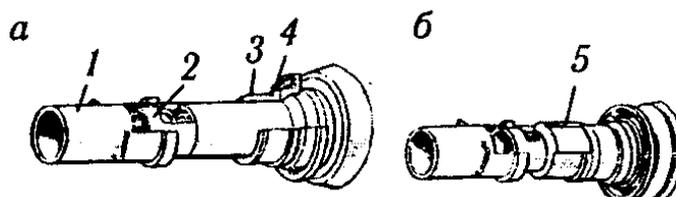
Расположение приспособлений при установке внутренних колец: а – заднего подшипника; б – переднего подшипника;
